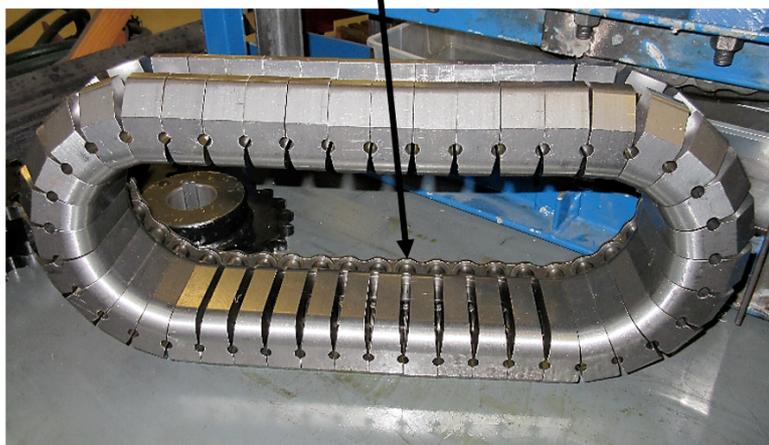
La cadena roscada, armada sobre una sola cadena de rodillos con pernos extendidos, dispuesta para recibir la segunda cadena en el primer plano de la foto
